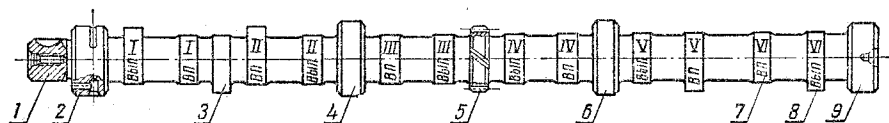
Распределительный вал шестицилиндрового двигателя ГАЗ-52-01:
